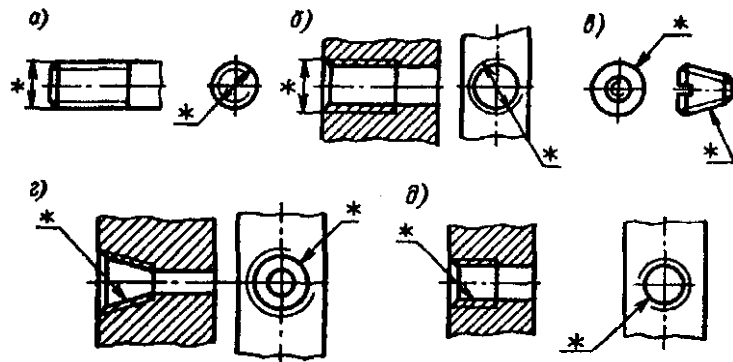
Обозначение резьбы: *a, б* — общее (*a* — для стержня; *б* — для отверстия); *в, г* — конической резьбы (*в* — для стержня; *г* — для отверстия); *д* — трубной цилиндрической резьбы; \* — место нанесения обозначения резьбы
